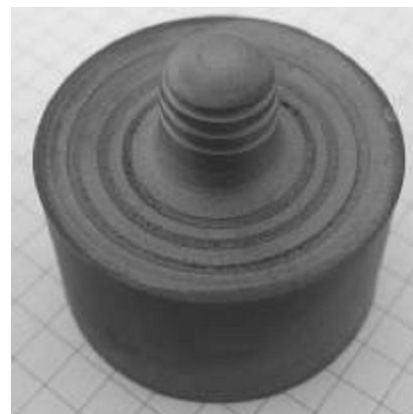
Общий вид инструмента для наплавки и сварки трением с перемешиванием
